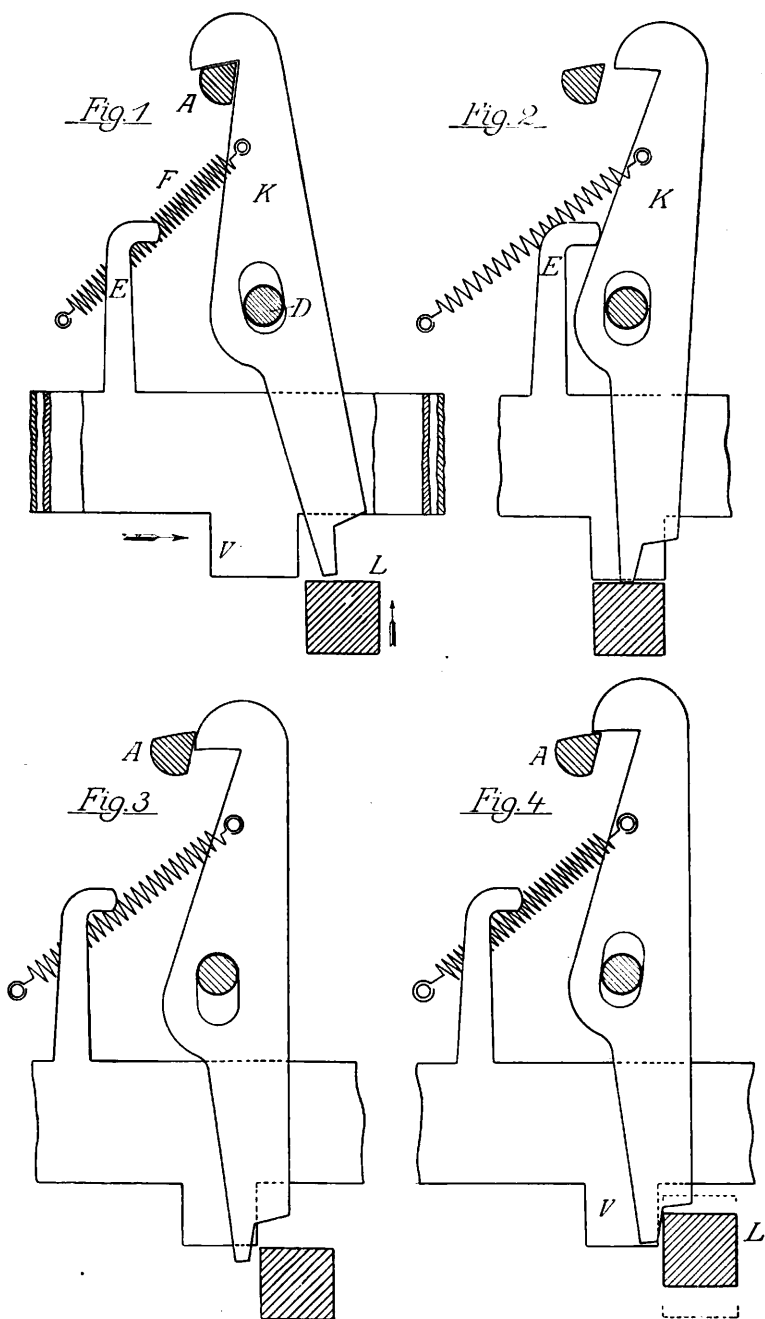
Mechanische Druckknopfsperre von M. Jüdel & Co., Braunschweig (1893).
